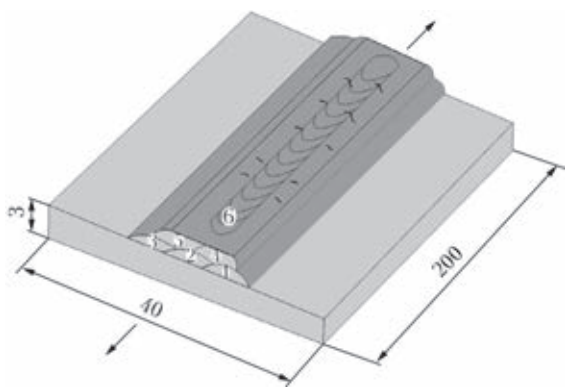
Схема проведения эксперимента по оценке трещиностойкости металла сварных швов со стабильно аустенитной структурой. Цифрами 1–5 указана очередность выполнения сварных швов при подготовке образца сваркой ТИГ с присадочной проволокой; 6 – контрольный шов с одновременной принудительной деформацией (ТИГ без присадки). Стрелками показано направление принудительного деформирования трещин промышленных сварочных проволок методом PVR-test.
